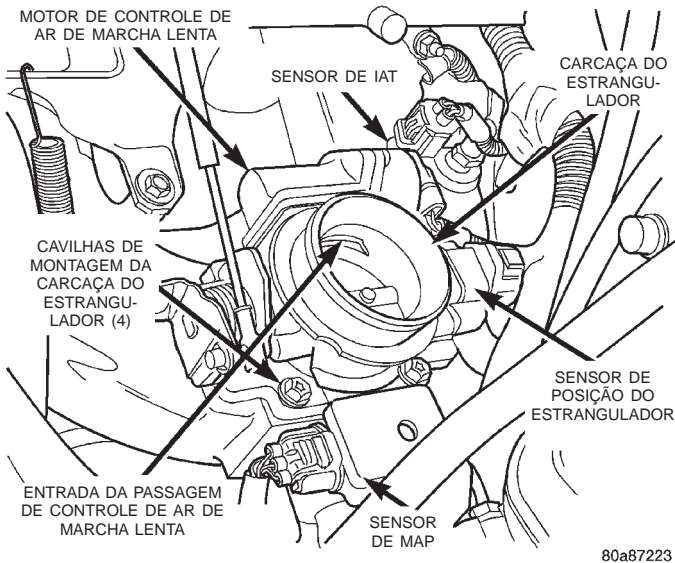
Localização dos Sensores e da Carcaça do Estrangulador—Motor 2.5L
